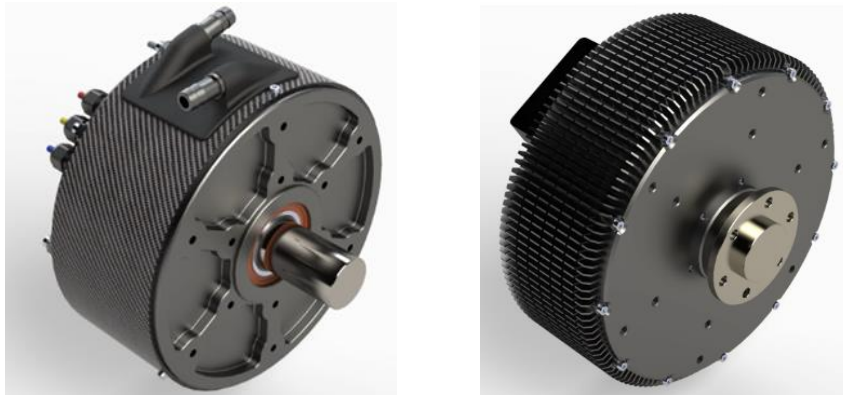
Usporiadanie statoru a rotoru u elektromotorov s axiálnym a radiálnym magnetickým tokom [18]
